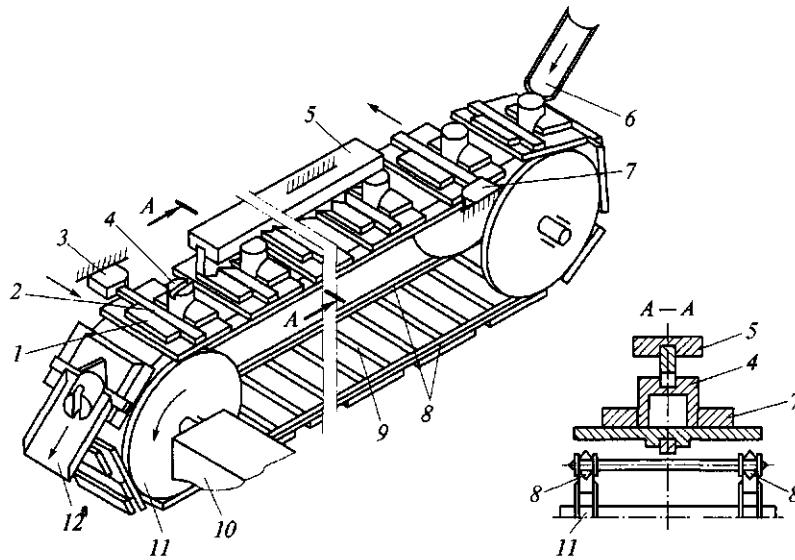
Принципиальная схема станка для непрерывного протягивания:
